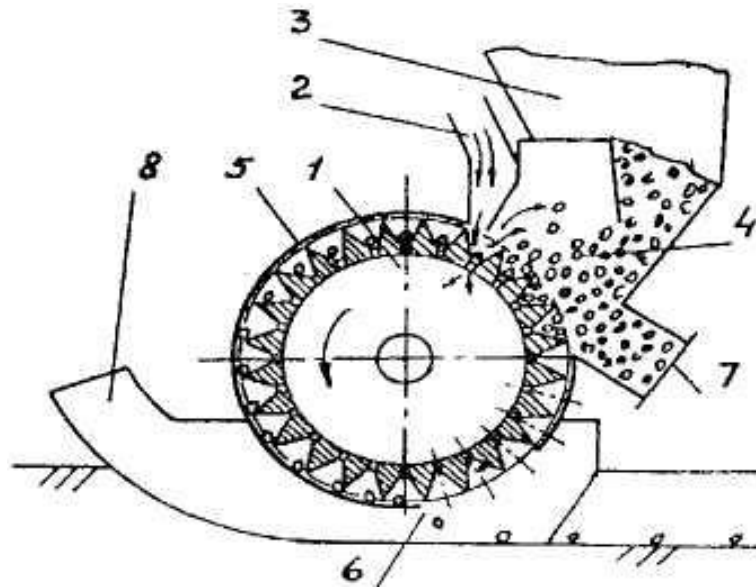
Схема пневматичного висівного апарата сівалки „Аеромат”: 1 - висівний диск; 2 - повітряний патрубок; 3 - бункер; 4 - приймальна камера; 5 - обмежувальний щиток; 6 - викидне вікно; 7 - розвантажувальний канал; 8 - сошник.
